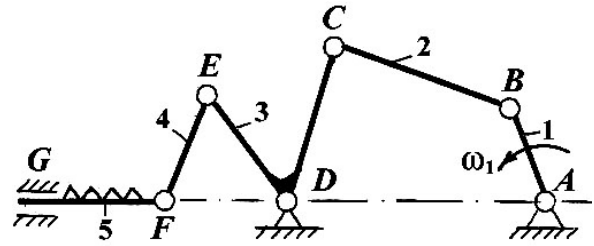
Механизм привода режущего аппарата зерноуборочного комбайна
